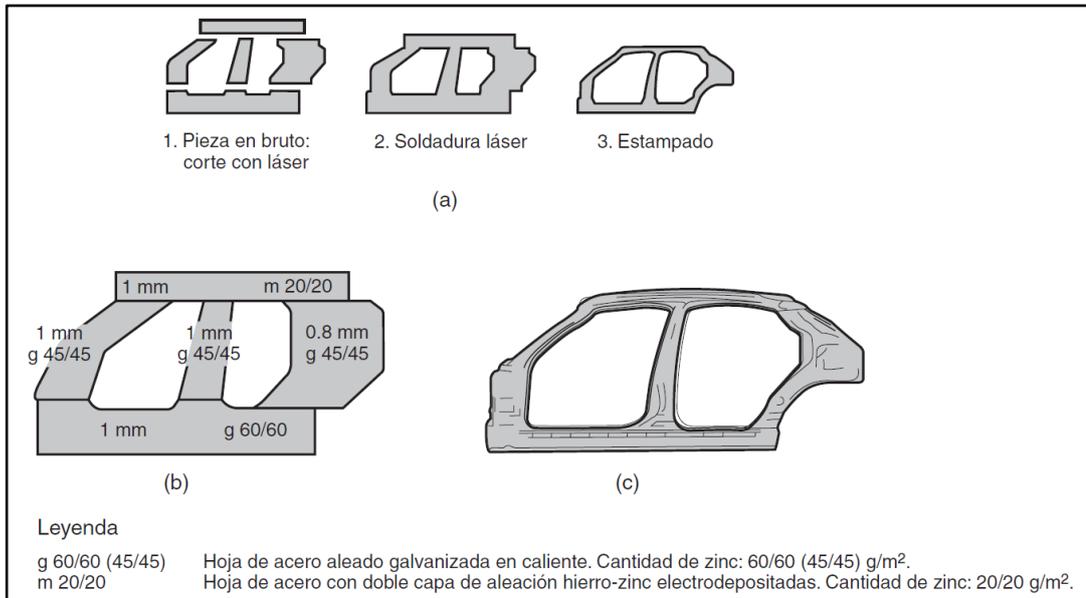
Producción de la pieza lateral exterior de una carrocería automotriz mediante soldado.
